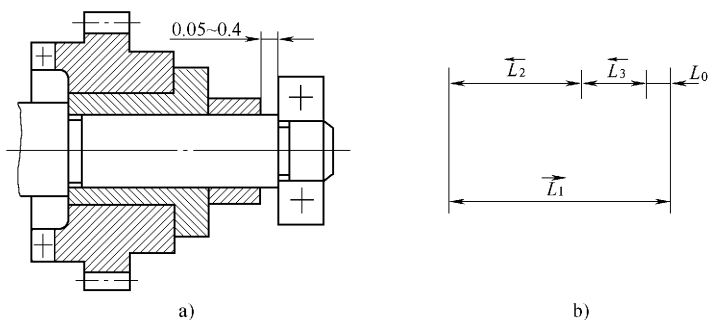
车床离合器齿轮轴的装配图及装配尺寸链图
